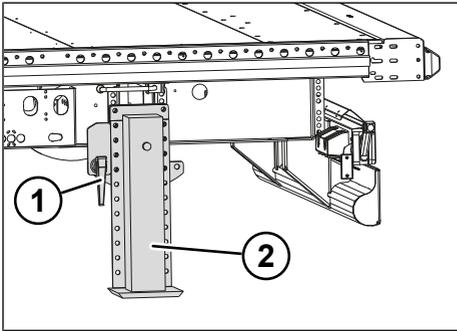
Dispositivo de apoio traseiro dobrado para baixo
